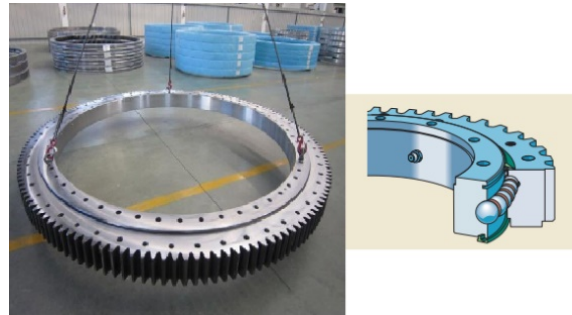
Corona giratoria de bolas con 4 puntos de contacto y engranaje exterior (Fuente: SKF)
